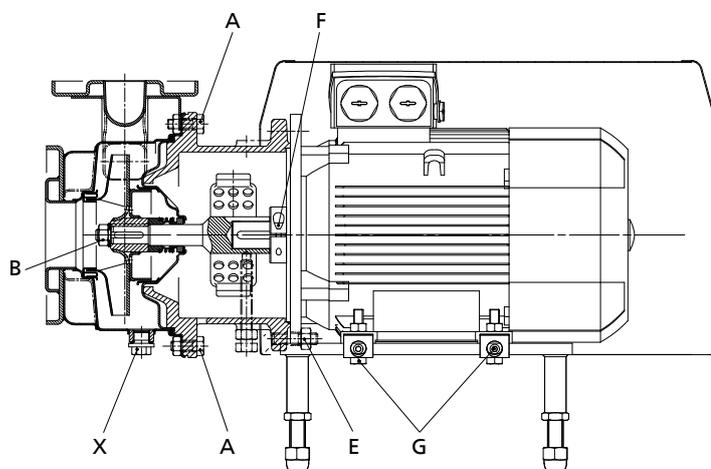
Ubicación de los tornillos para Etachrom B 050-025-125.1, 050-025-125, 050-025-160, 050-025-200, 050-032-125.1, 050-032-125, 050-032-160, 050-032-200, 065-040-125, 065-040-160, 065-040-200, 065-050-125, 065-050-160
